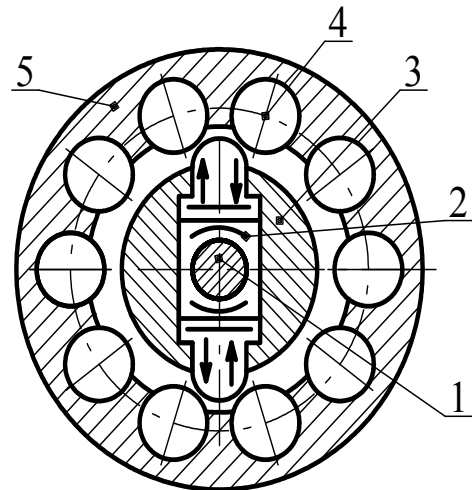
Схема ротаційно-кувальної машини: 1 – заготовка; 2 – бойок; 3 – шпиндель; 4 – ролик; 5 – обойма
